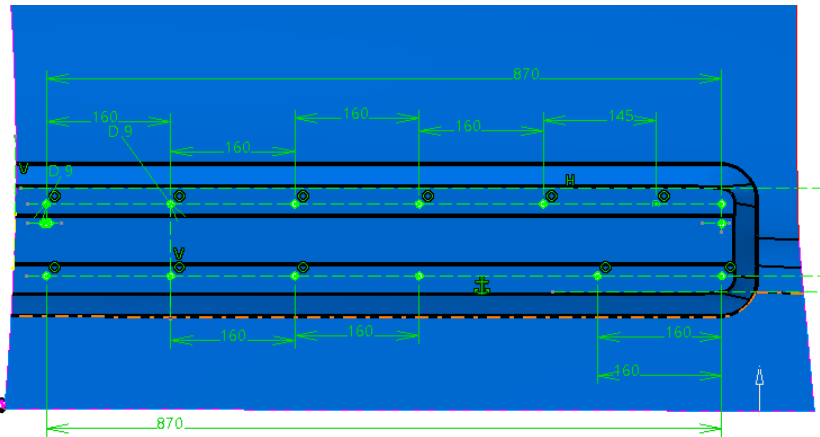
Croquis para el planteamiento de las fijaciones.
